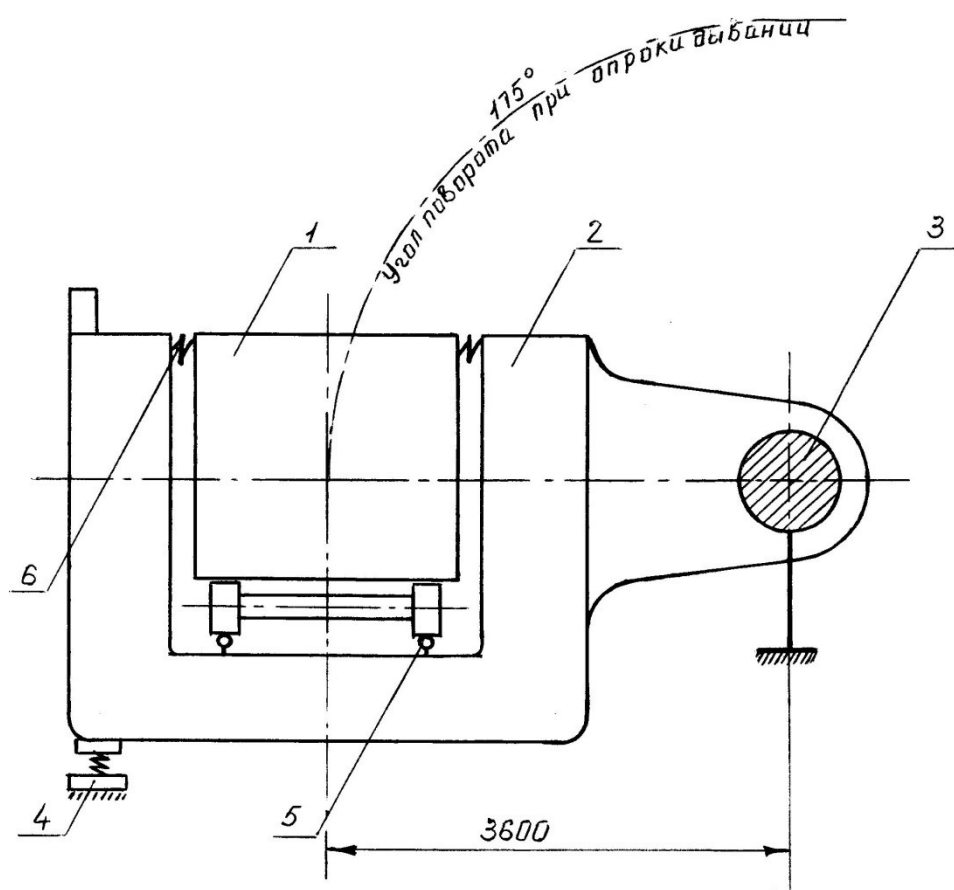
Схема вагоноопрокидывателя с боковой разгрузкой вагона
